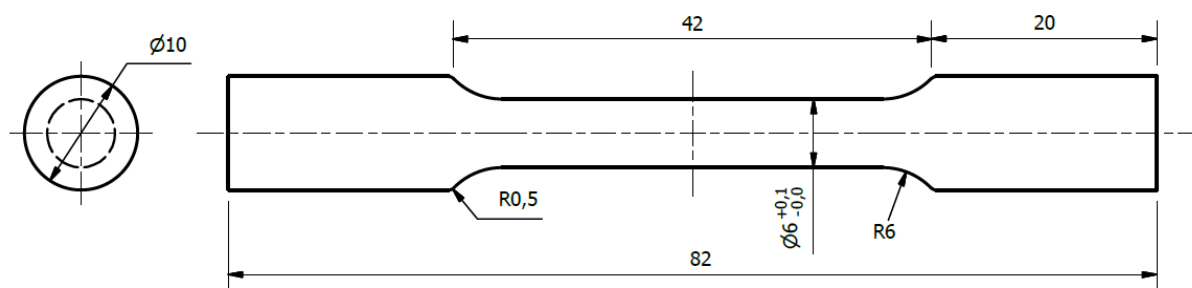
Dimensões dos corpos de prova de seção circular usados nos ensaios de tração.
